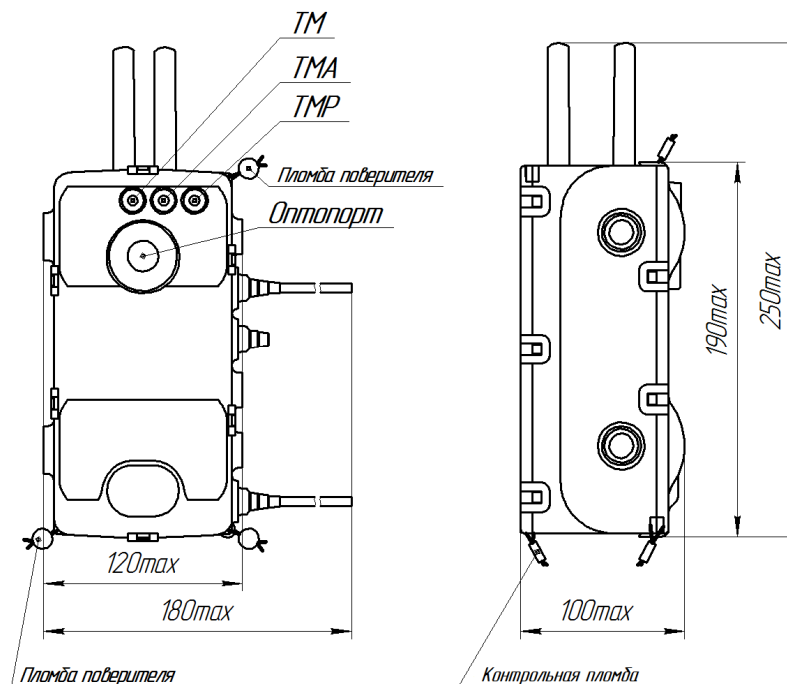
Габаритные и установочные размеры и расположение индикаторов счетчиков
